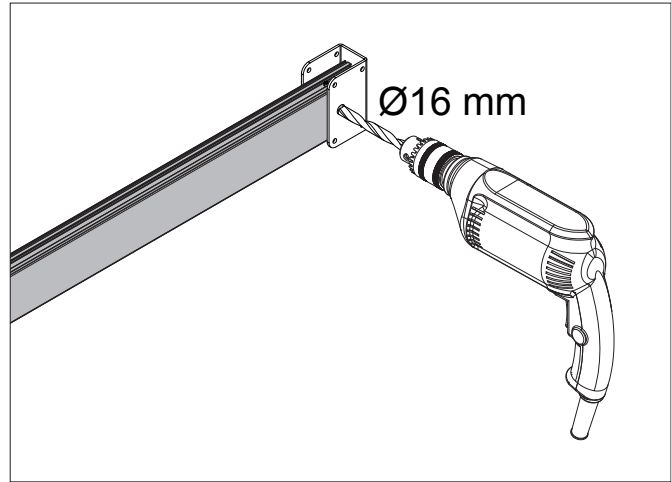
INSTALLAZIONE ASTA FISSA / FIX BAR INSTALLATION
